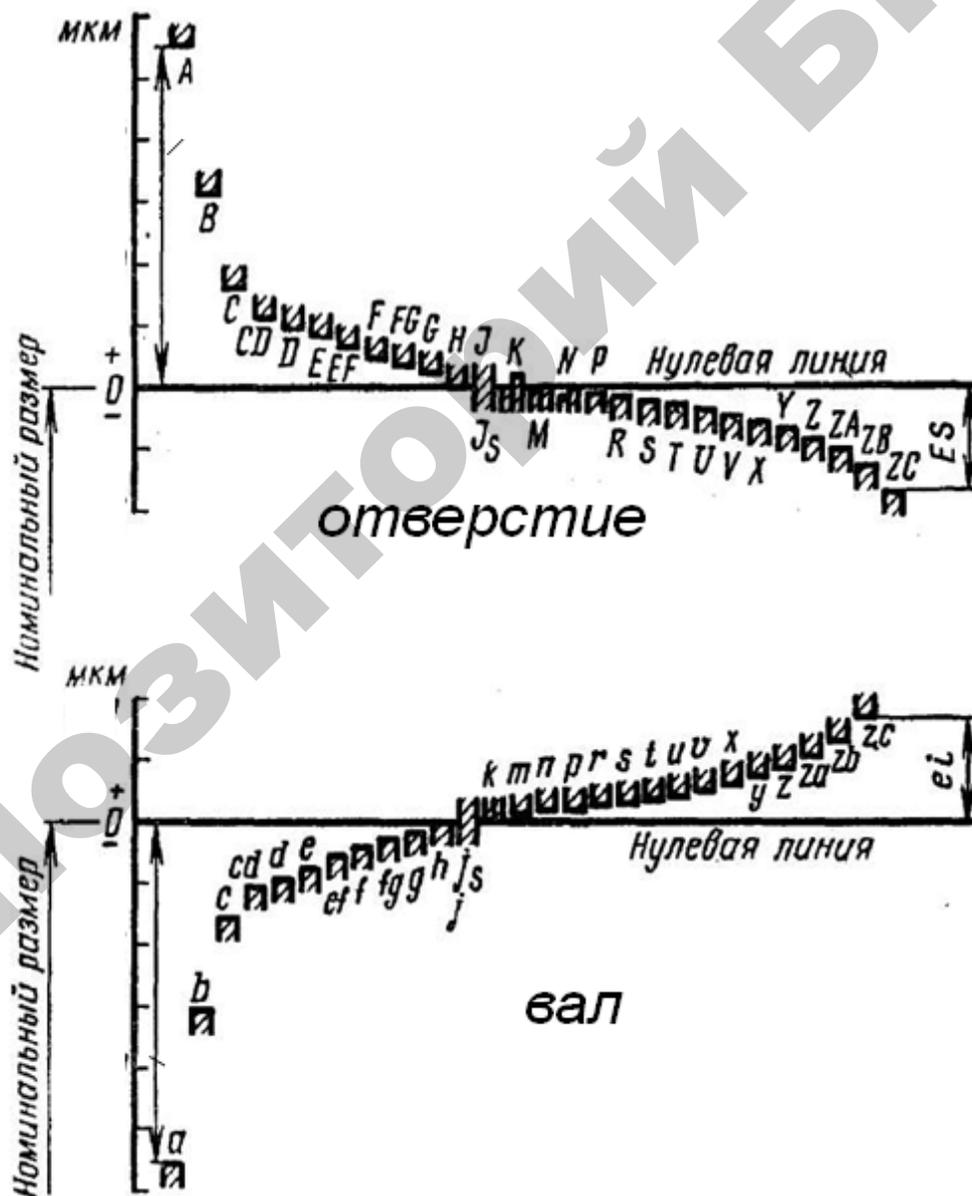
Схемы расположений полей допусков валов и отверстий
